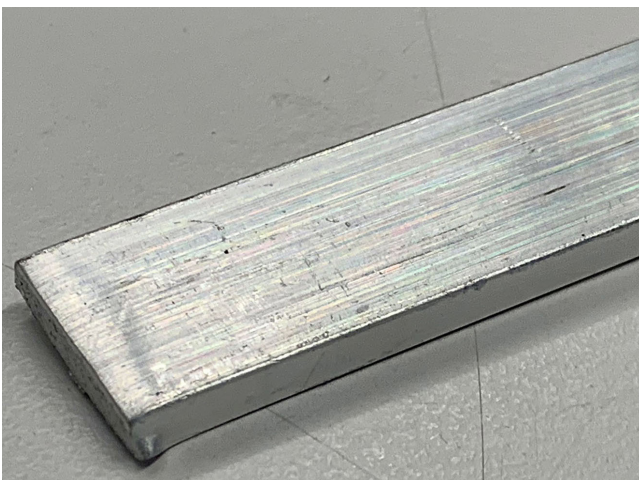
Stranggepresstes, schäumbares Aluminiumhalbzeug aus Aluminiumlegierungsspänen, Querschnitt 20 mm x 5 mm. Foto: Fraunhofer IWU
